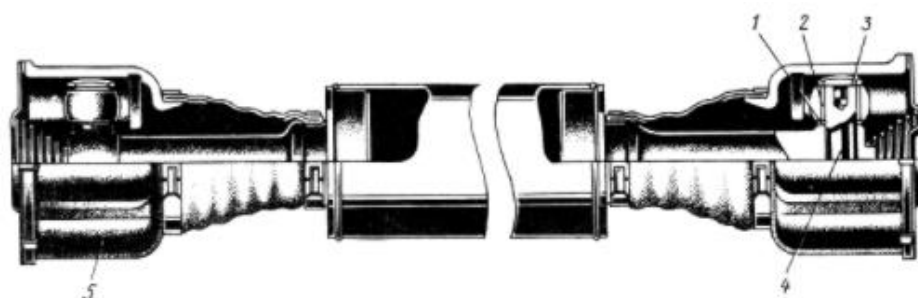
Карданный вал с двумя универсальными шарнирами: 1 – сферический ролик; 2 – подшипник игольчатого типа; 3 – центрирующие заглушки; 4 – пустотелый палец; 5 – корпус шарнира
